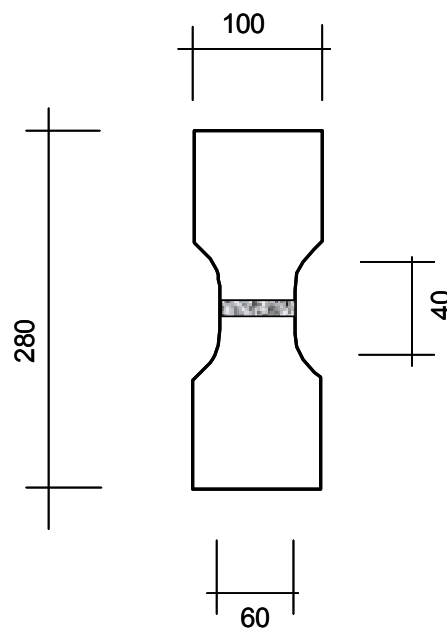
Proben für die Schweißverbindung des Untergurts; Maße in mm
